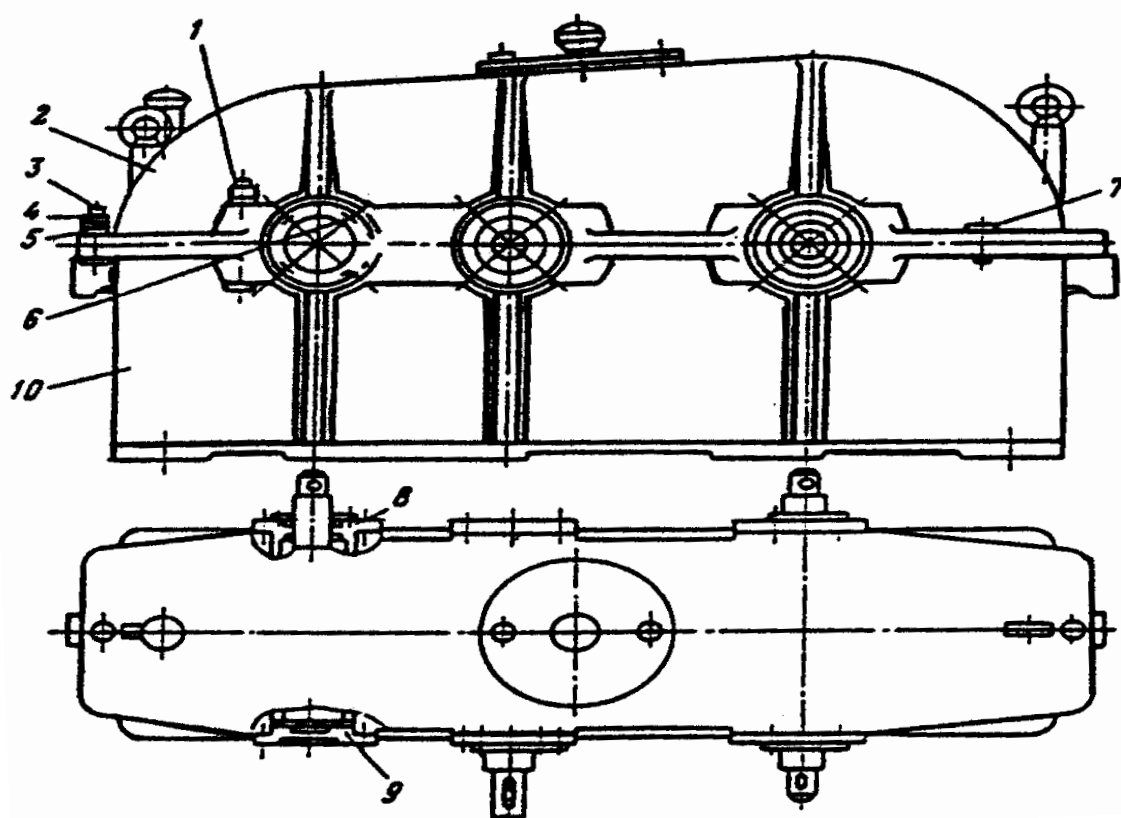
Двухступенчатый цилиндрический редуктор
